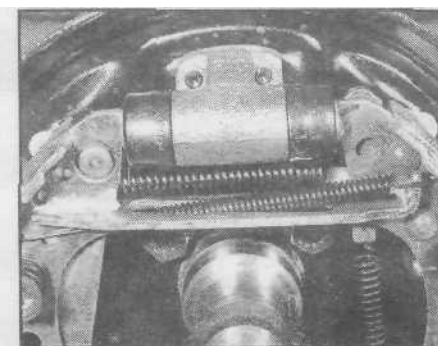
Колесный цилиндр, верхняя стяжная пружина и разжимное устройство
